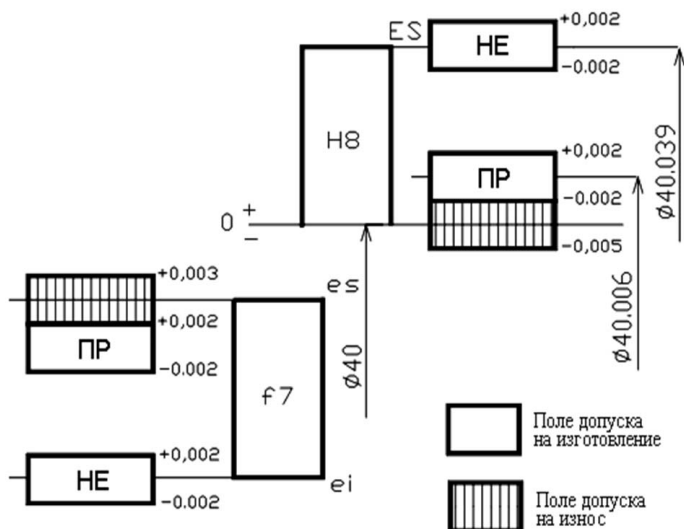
Расположение полей допусков предельных калибров
